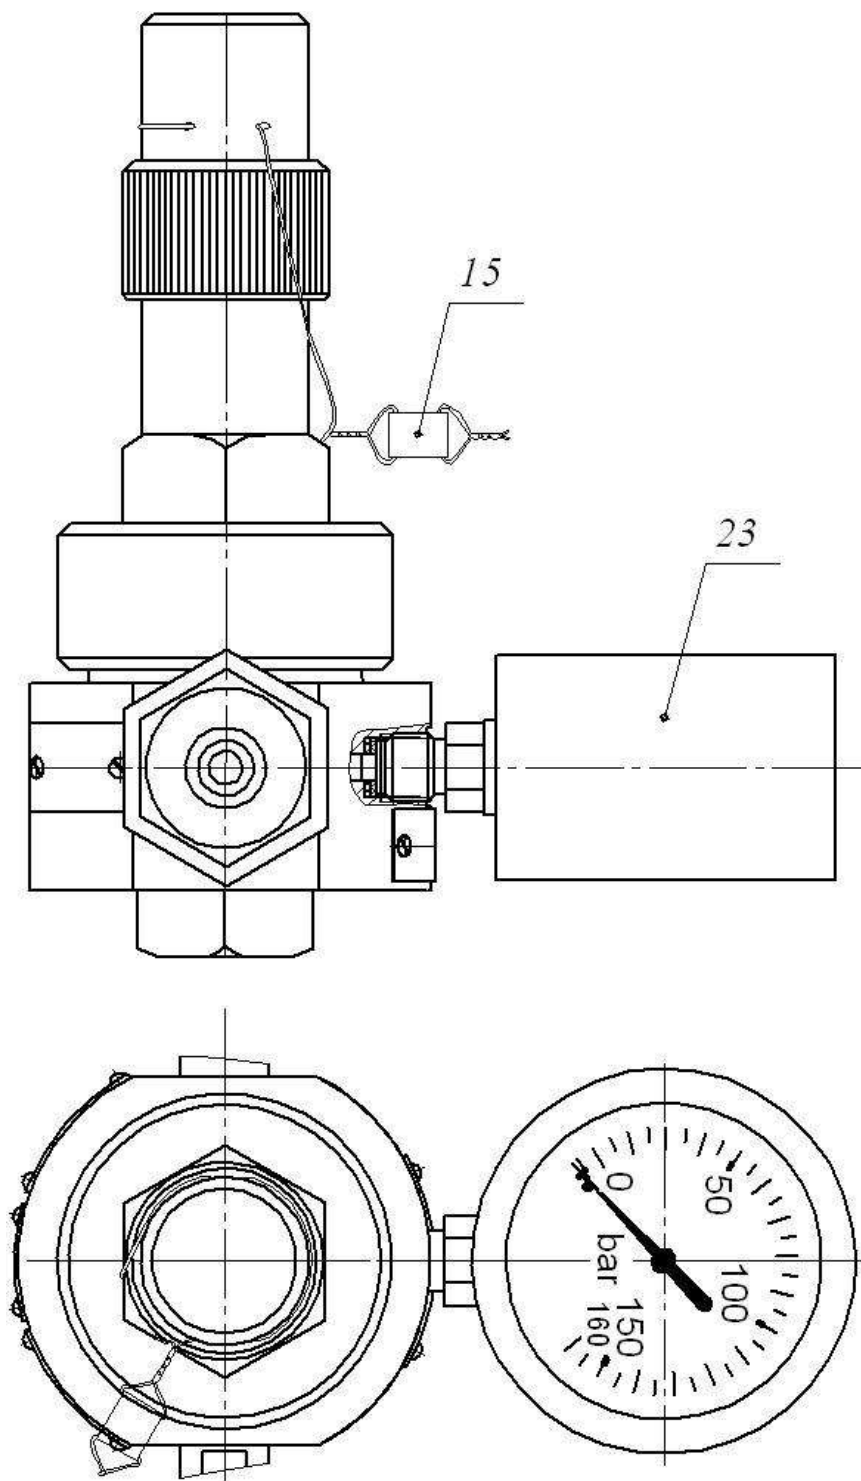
Конструкция редукторов РДФ-7...РДФ-7-9
